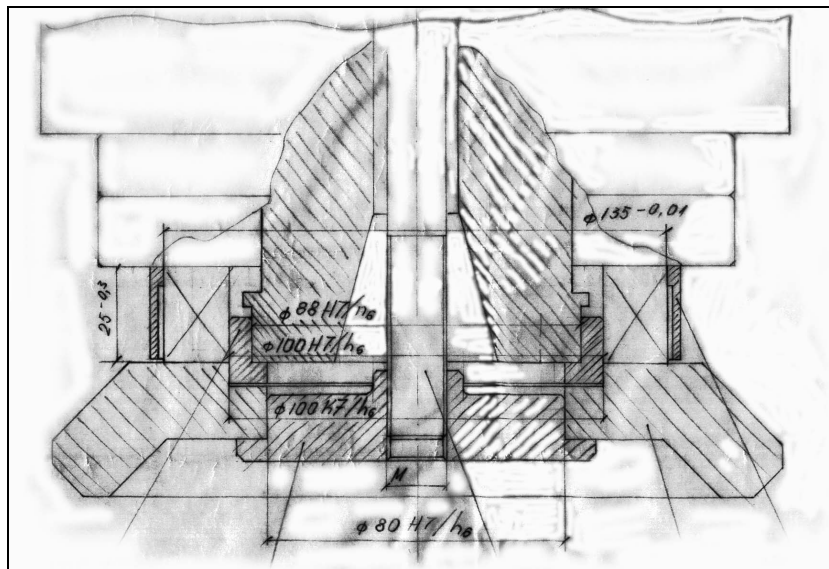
Эскиз экспериментального узла базирования корпуса фрезы торцом по упорному подшипнику
